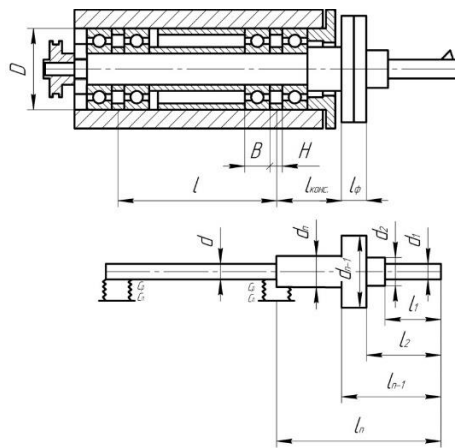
Конструктивна і статична розрахункові схеми шпindelьного вузла з борштангою¹⁰⁰⁹.
